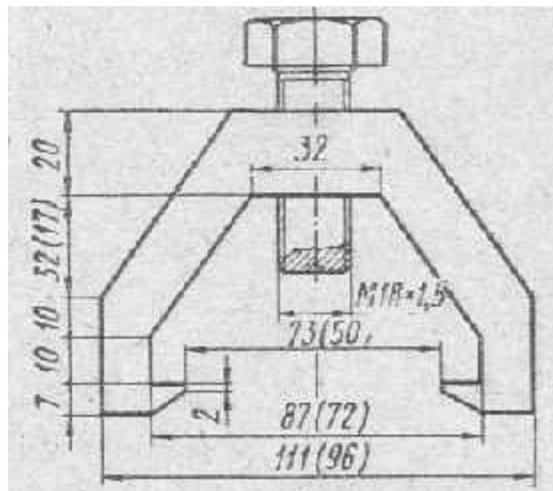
Съемник для снятая ведущей звездочки моторной передачи мотоцикла ЯВА-350 (в скобках указаны цифры для съемника звездочки мотоцикла ЯВА-250)
